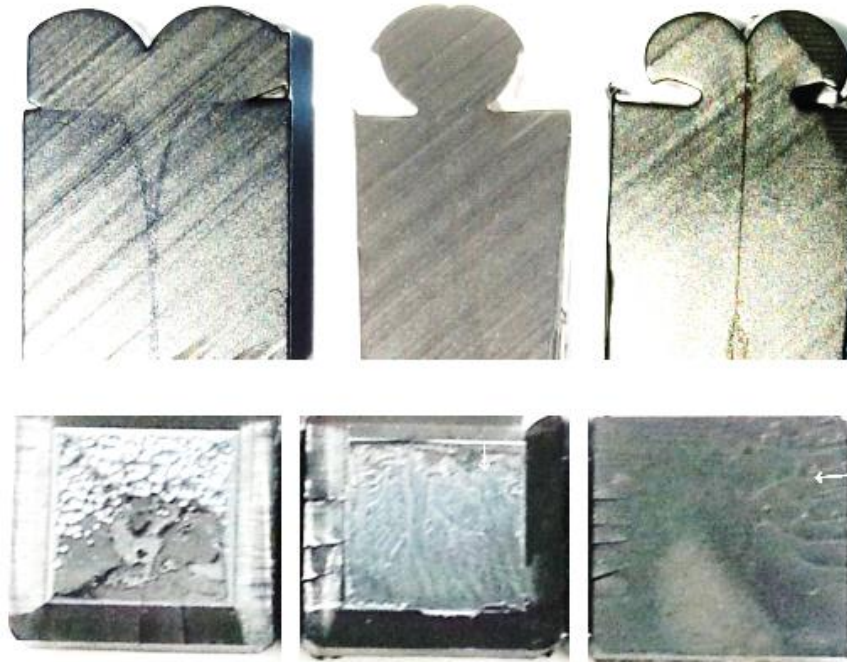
Image optique de bourrelet de soudure [21].
